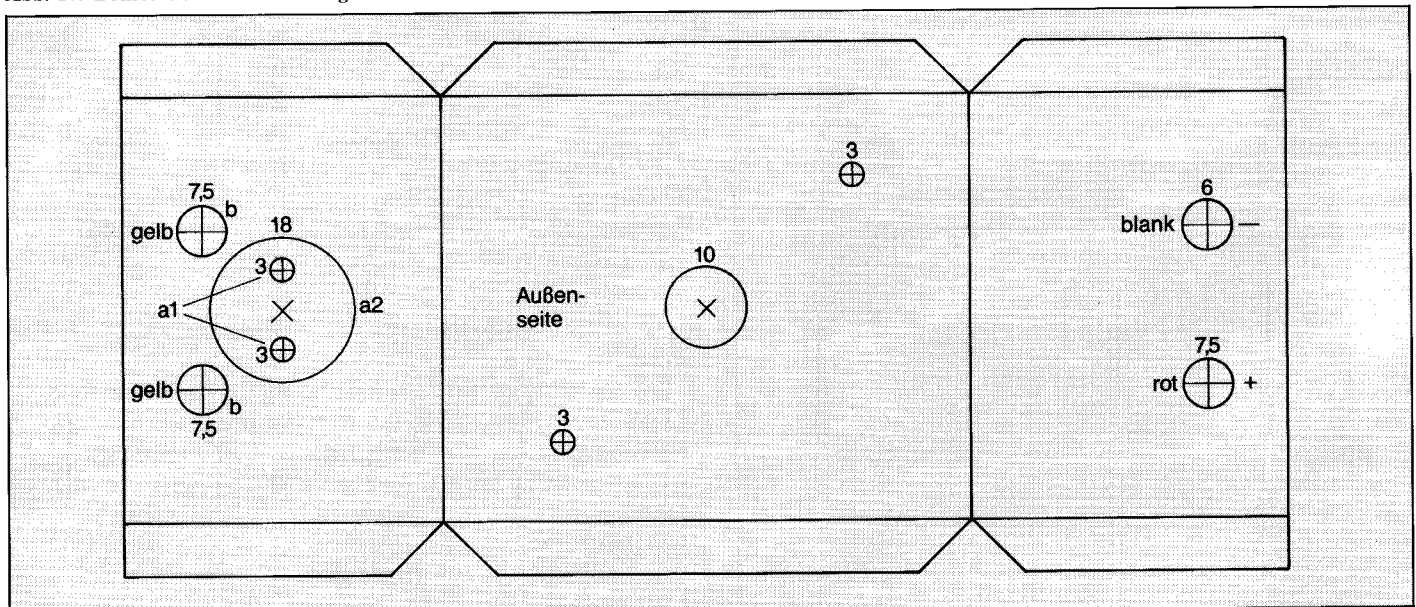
Wandler SQ 40T in Halterungen mit eingebauten Bananenanschlußbuchsen
